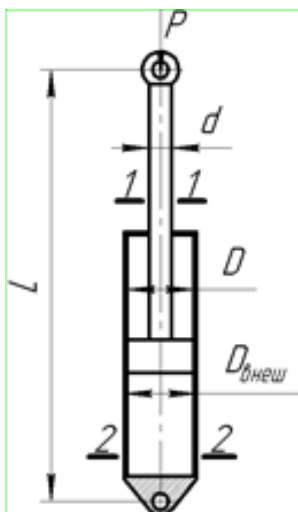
Расчетная схема для определения устойчивости гидроцилиндра.
